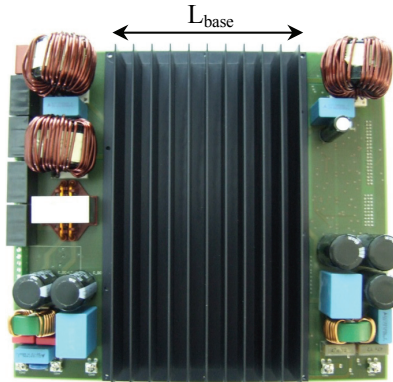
Face arrière du prototype réalisé - intégration mécanique retenue
